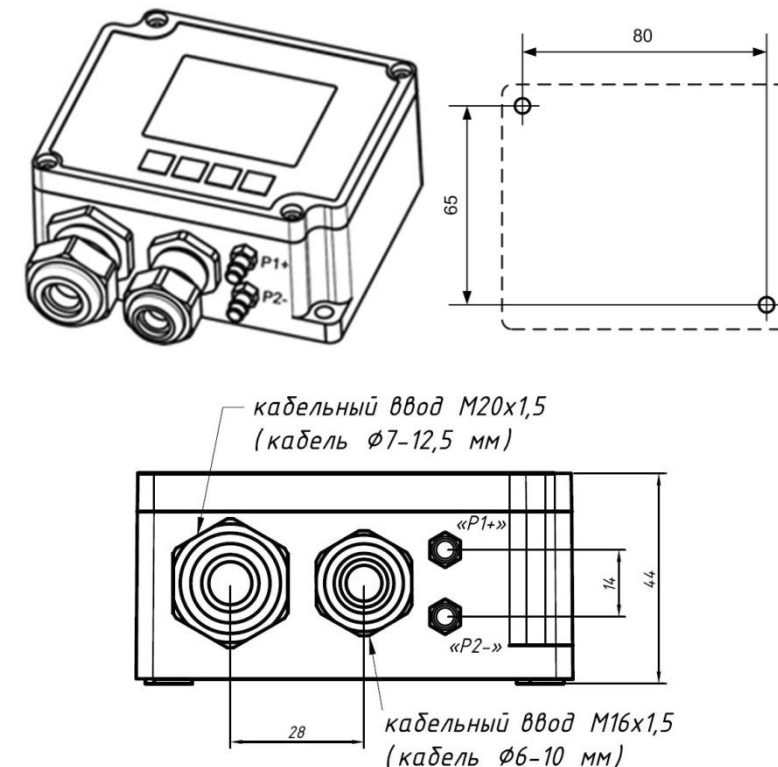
Вид корпуса изделия и разметка отверстий для крепления
